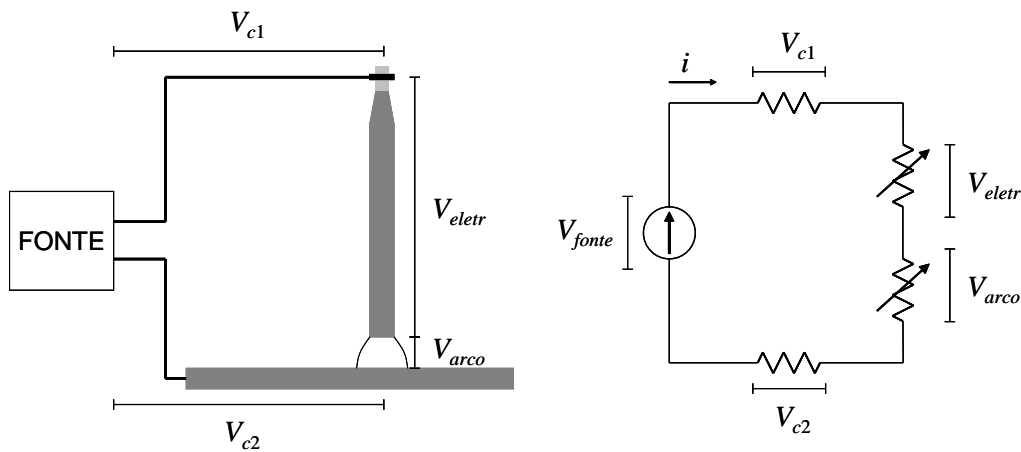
Circuito elétrico da soldagem com eletrodo revestido.
